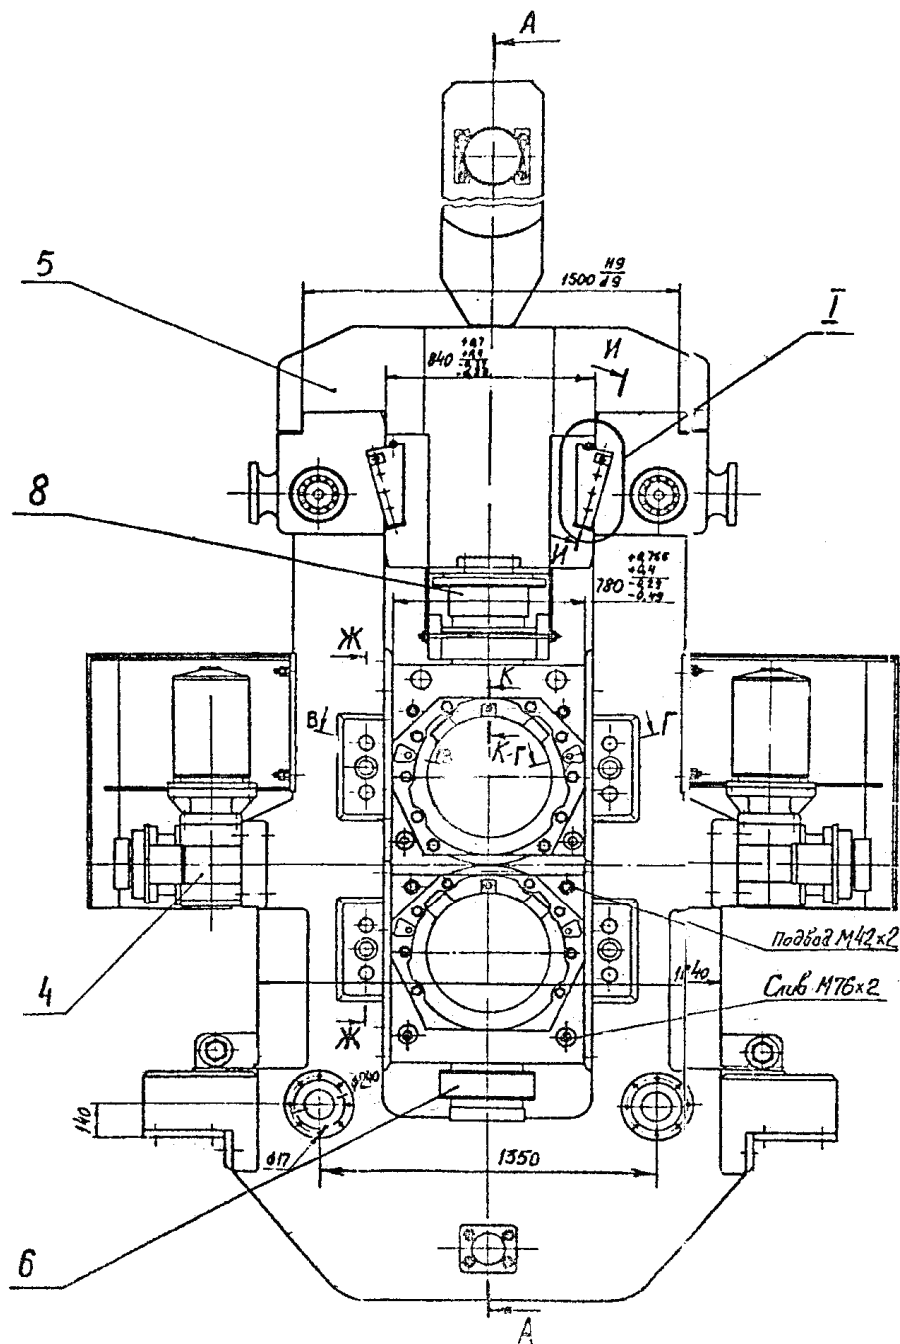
Кліть 730 ПН. Загальний вид (вид збоку)
